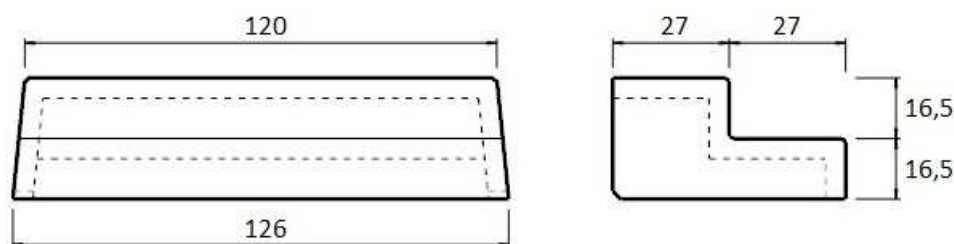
Dimensiones del escalón (dimensiones en mm)
